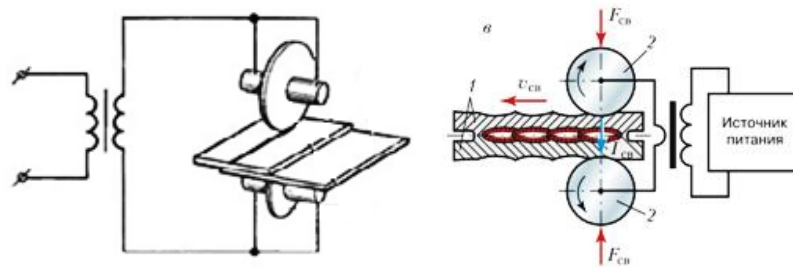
Схема шовной (роликовой) сварки
